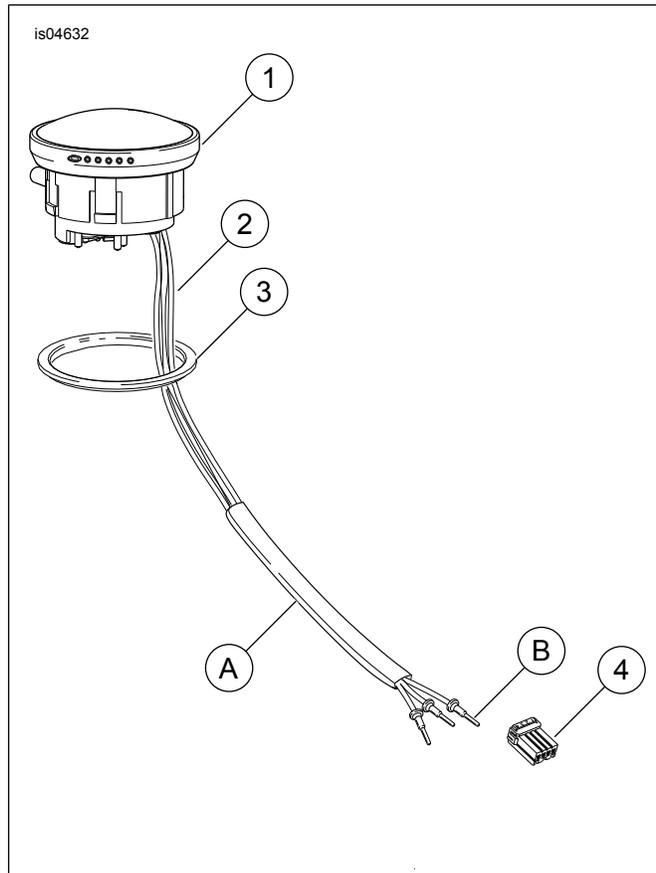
Pièces détachées : kit de jauge de carburant à DÉL
